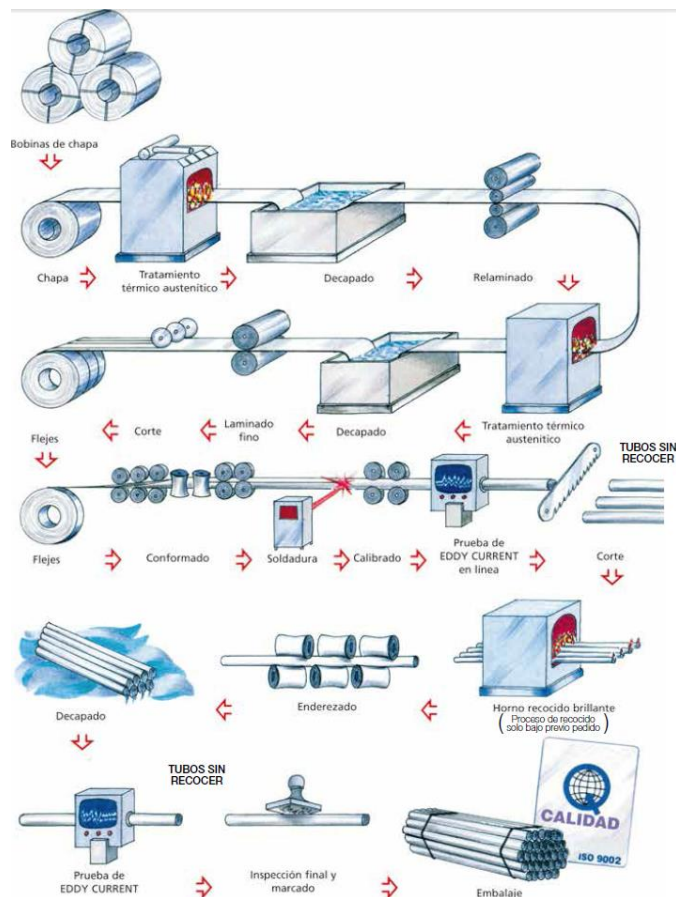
Proceso de fabricación del tubo soldado.
